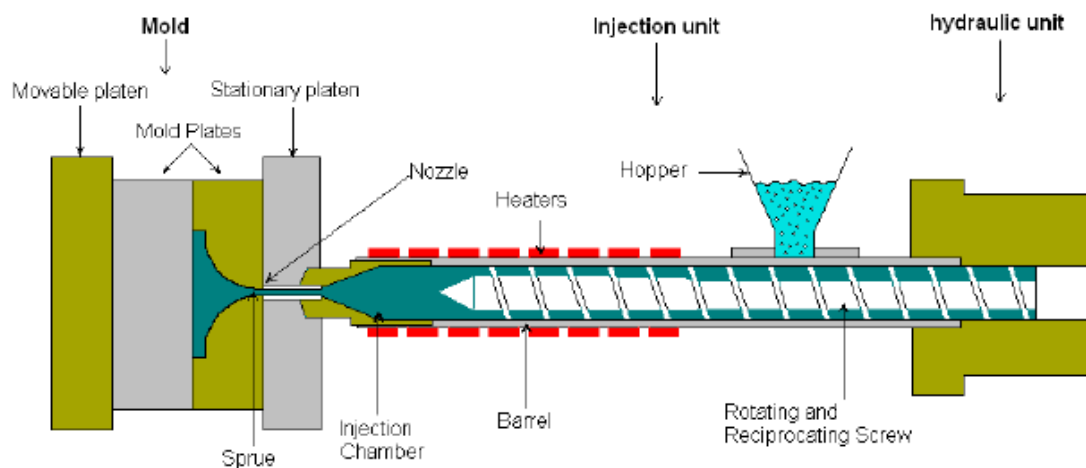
Une seule machine de moulage par injection à vis (The Santa Clara University Design Center 1998).
